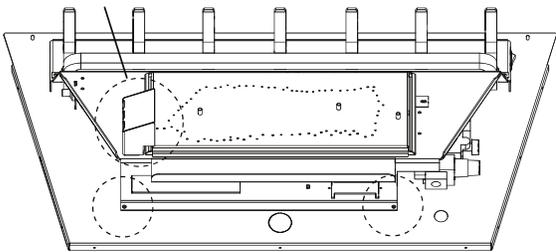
Vue Arrière de l'Assemblage de Soupape
